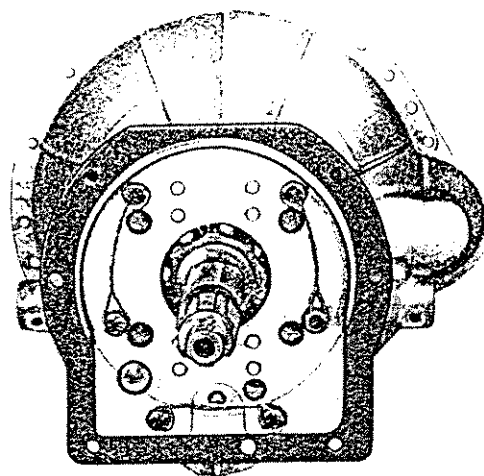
Sicherung der Schrauben auf der Anschlußplatte mit Draht
